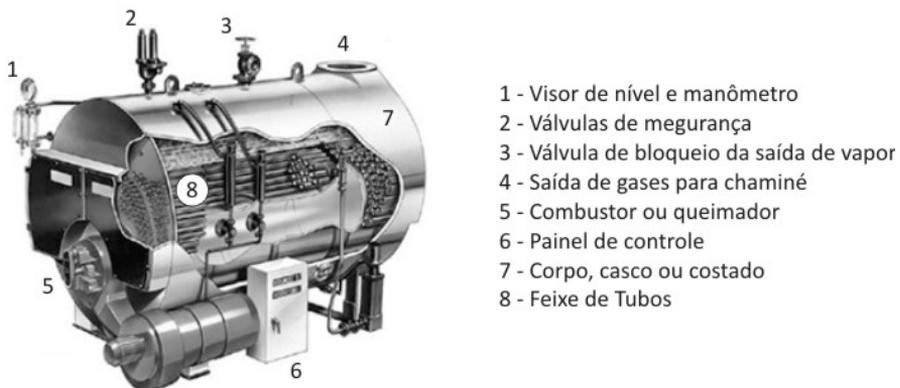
Desenho esquemático de caldeira flamotubular e principais componentes.
